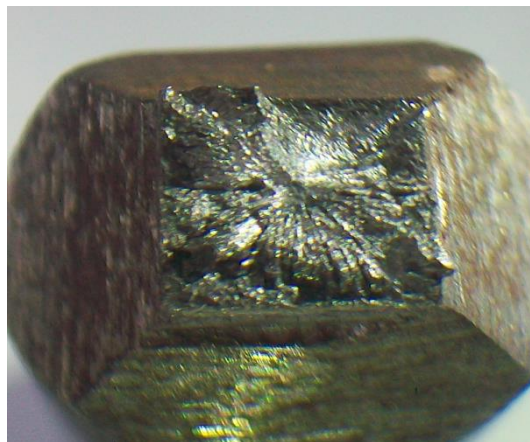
Sección transversal de la rotura de la probeta 6.
